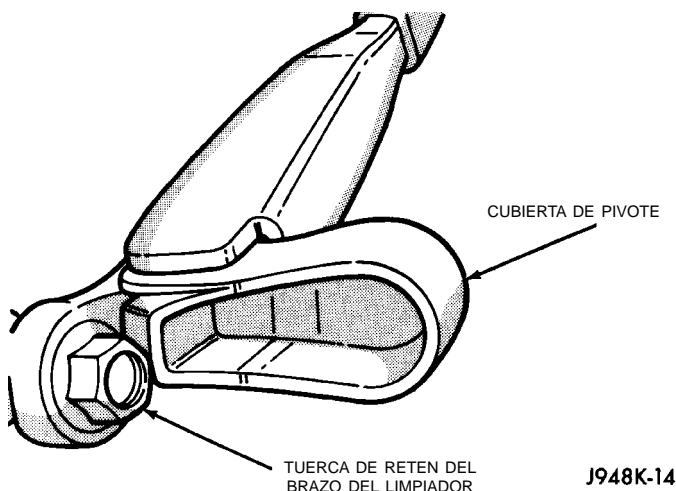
Desmontaje/instalación del brazo del limpiador trasero
